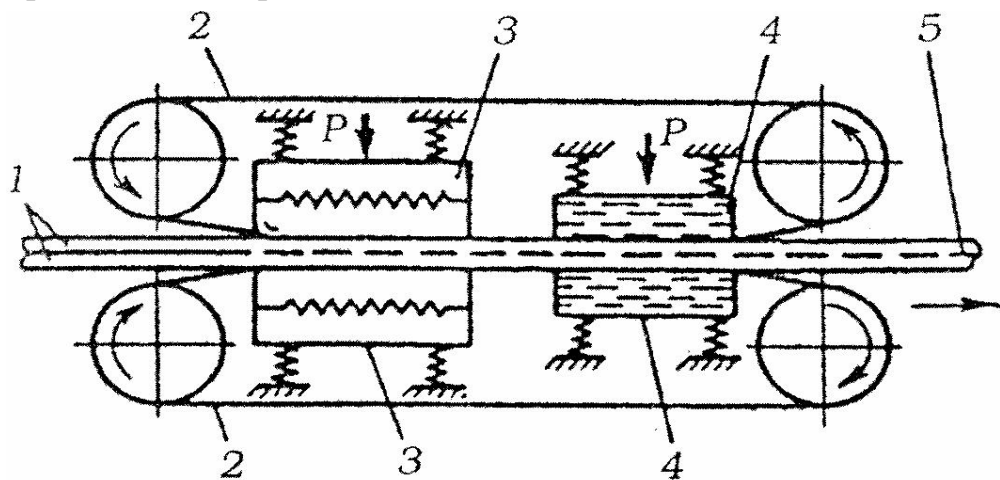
Схема двохстороннього контактно-теплового зварювання із застосуванням стрічки: 1 -матеріал, що зварюється; 2 - стальна стрічка; 3 - нагрівальні губки; 4 - охолоджуючі губки; 5 - зварний шов
